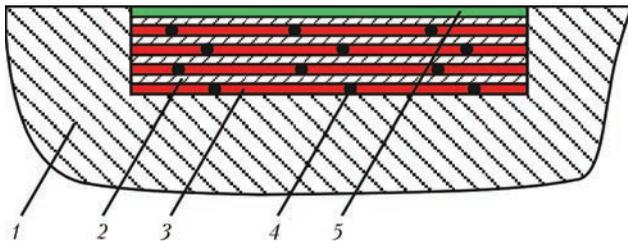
Клееварной метод восстановления посадочного места подшипника в корпусной детали: 1 — опора; 2 — многослой из тонколистовой стали 05кп; 3 — наполнитель межслоистого пространства — анаэробный герметик; 4 — сварная точка; 5 — финишный слой композита
